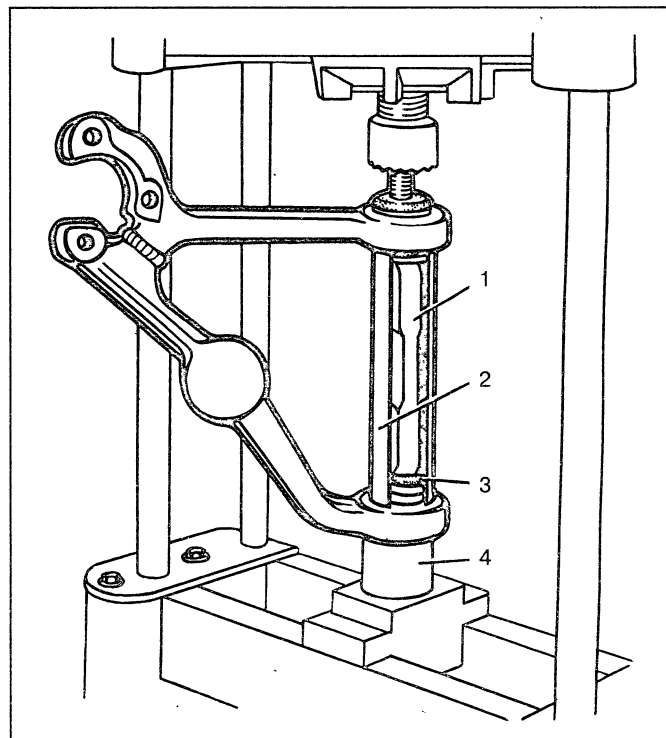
Выпрессовка шарниров верхнего рычага: 1 – ось рычага; 2 – приспособление 67.7823.9527; 3 – шарнир; 4 – оправка А.74177/1
